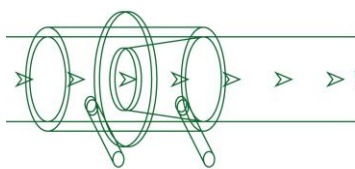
Einschweiß-Montageteil (Schweißmuffe)
